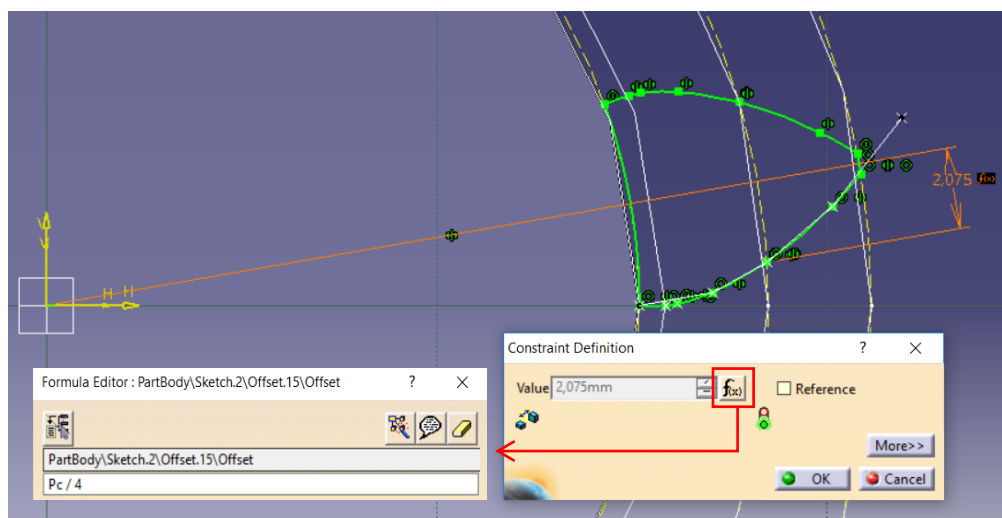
Inputs geométricos para el diseño del engranaje (Fuente: propia)
